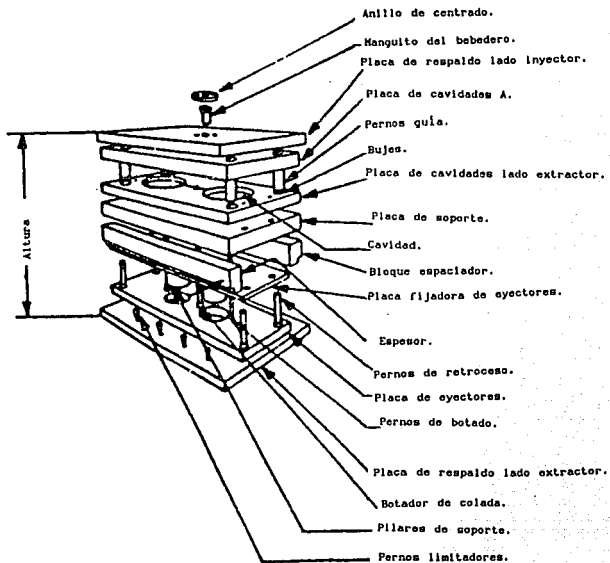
Vista explosiva de la configuración de un molde de Inyección [10].
